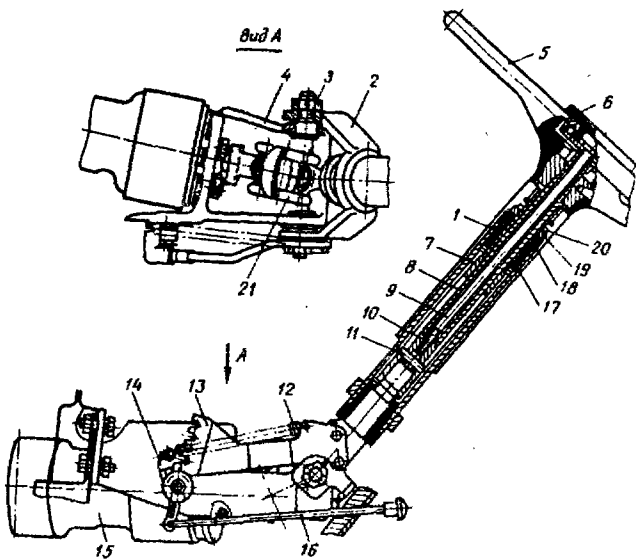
Колонка рулевого привода тракторов семейства МТЗ: 1 - труба рулевой колонки; 2 - вилка; 3 - винт; 4 - кронштейн; 5 - рулевое колесо; 6 - маховичок; 7 - промежуточный вал; 8 - вал; 9 - винт маховичка; 10, 19 - гайки; 11 - штифт; 12 - пружина сектора; 13 - сектор; 14 - фиксатор; 15 - насос-дозатор; 16 - тяга фиксатора; 17 - втулка; 18 - амортизатор; 20 - контргайка; 21 - двойной карданный шарнир
